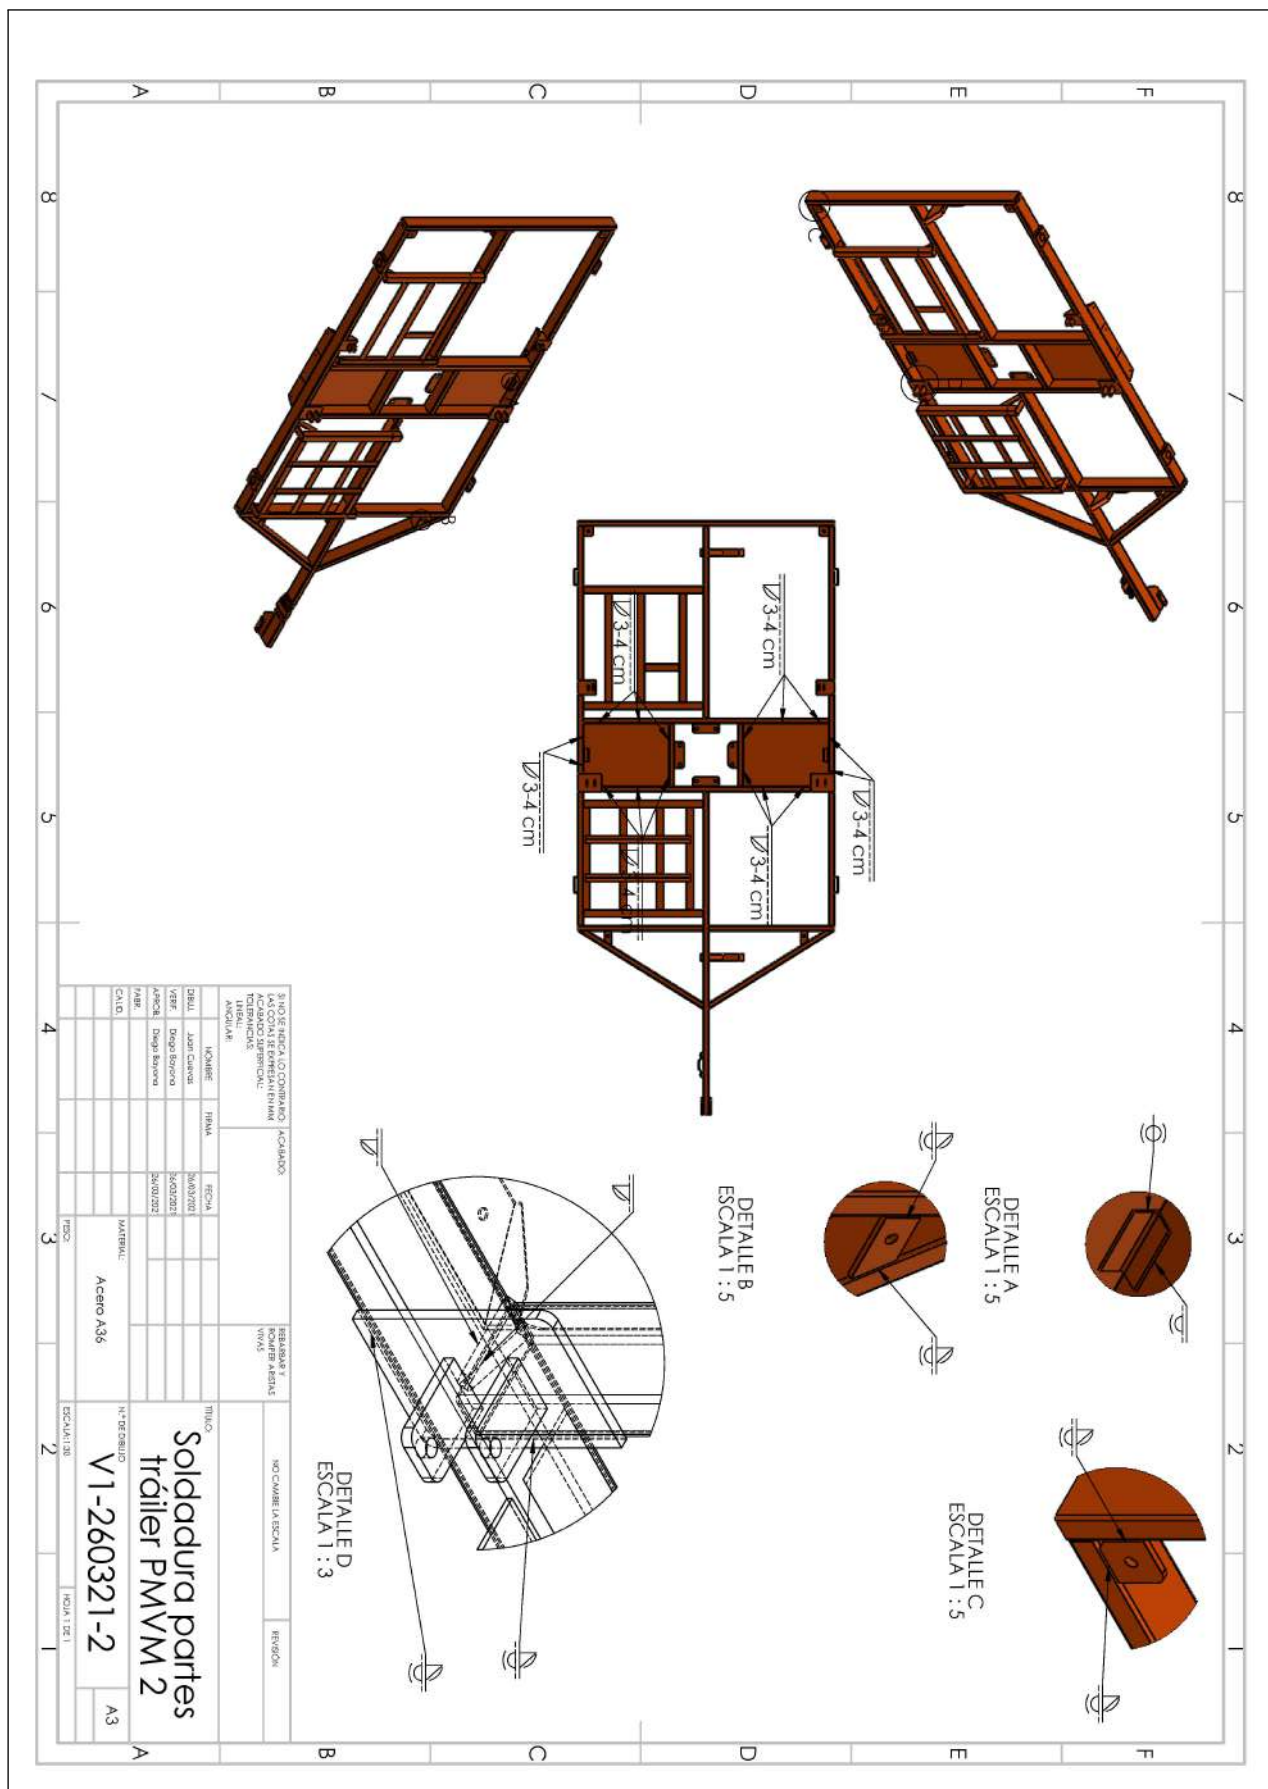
Soldadura partes tráiler PMVM 2.
